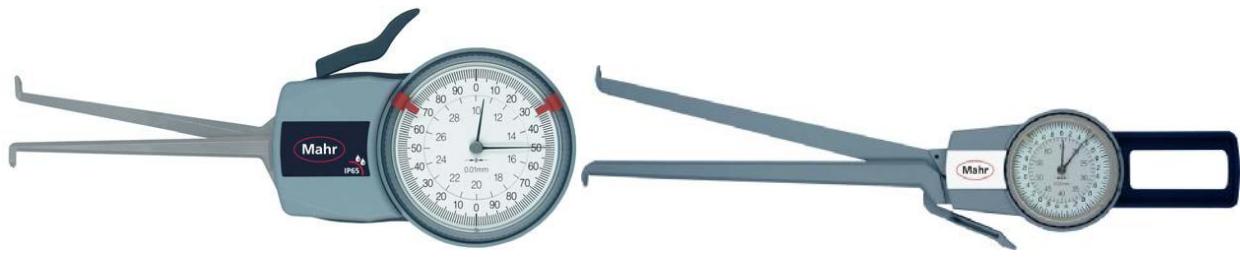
Внешний вид калибров-скоб MaraMeter 838 EI
